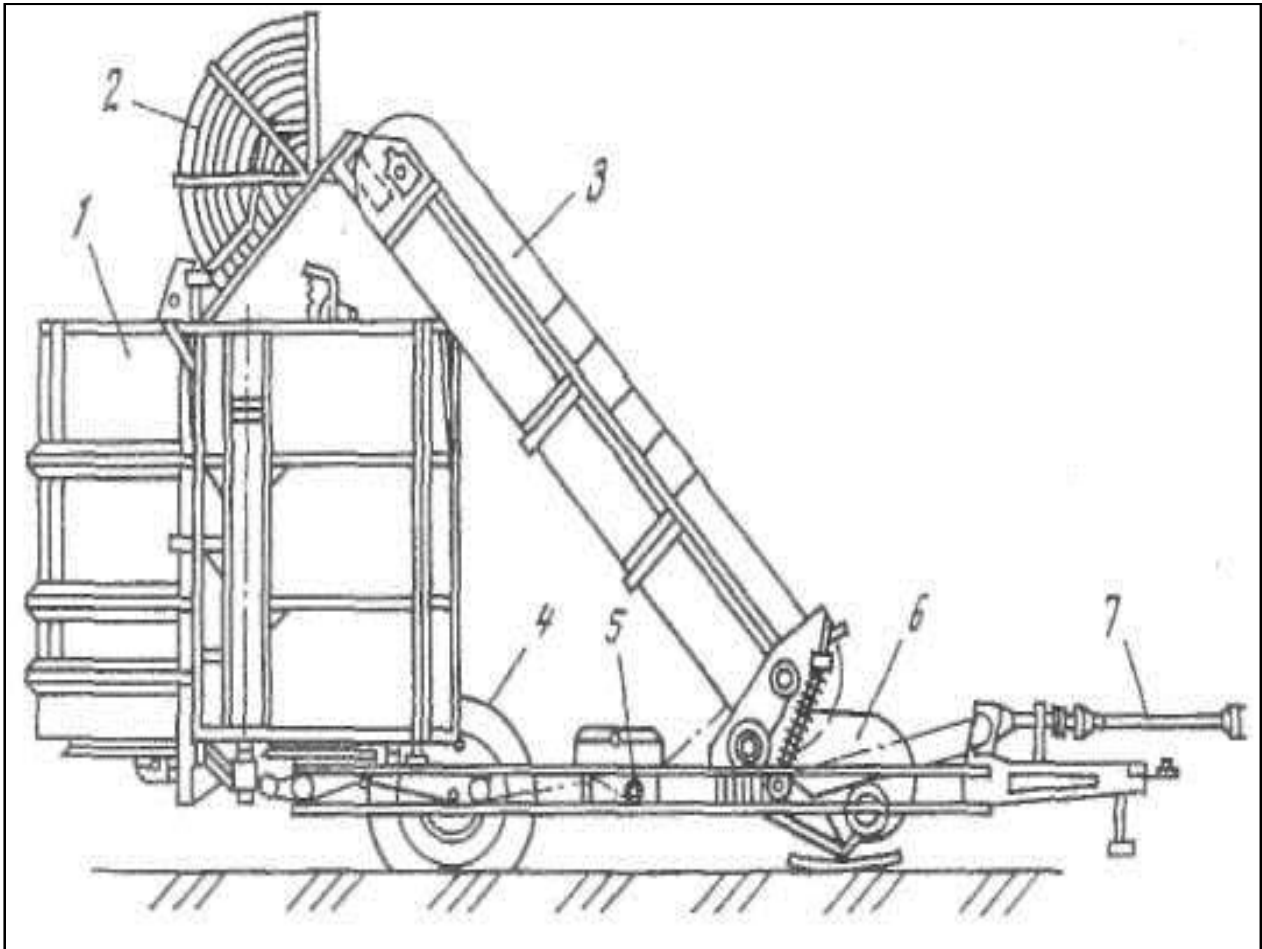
Подборщик-копнитель ПК-1.6А: 1 – копнитель; 2 – промежуточный накопитель; 3 – цепочно-планчатый транспортер; 4 – ходовое колесо; 5 – рама; 6 – барабанный подборщик; 7 – механизм привода
